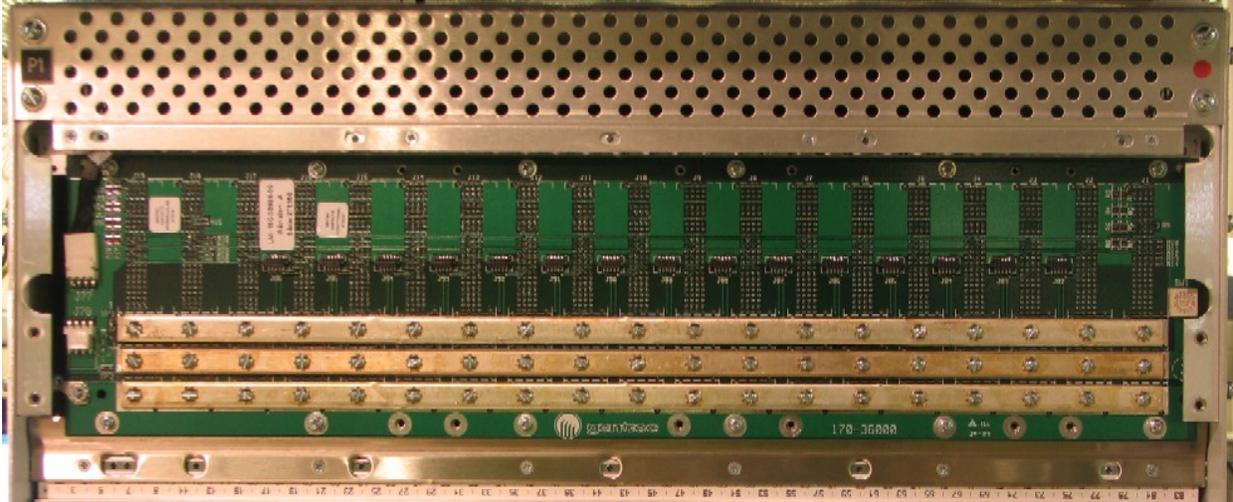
Vue de la carte CMA3 (dernière génération)
